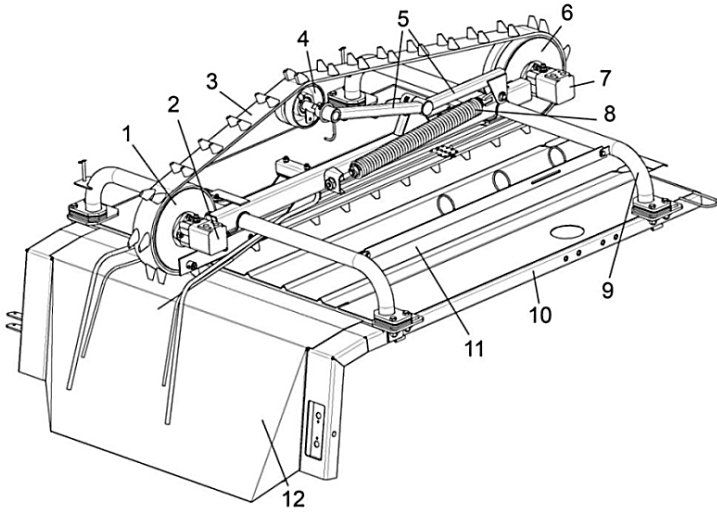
Расстилочное устройство: 1, 6 – шкивы; 2, 7 – гидромоторы; 3 – расстилочный транспортер; 4 – натяжной ролик; 5 – рычаг; 8 – пружина; 9 – опора; 10 – рама; 11 – расстилочный стол; 12 – скат
